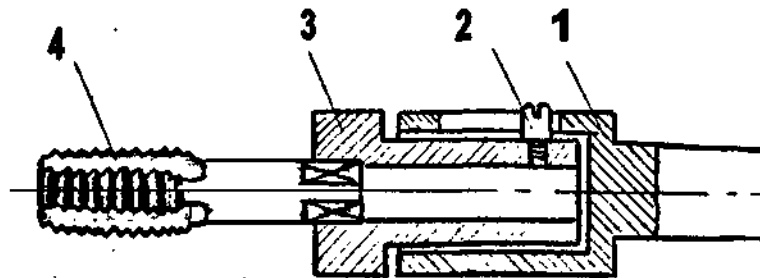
Качающаяся самовыдвижная оправка (метчикодержатель).
